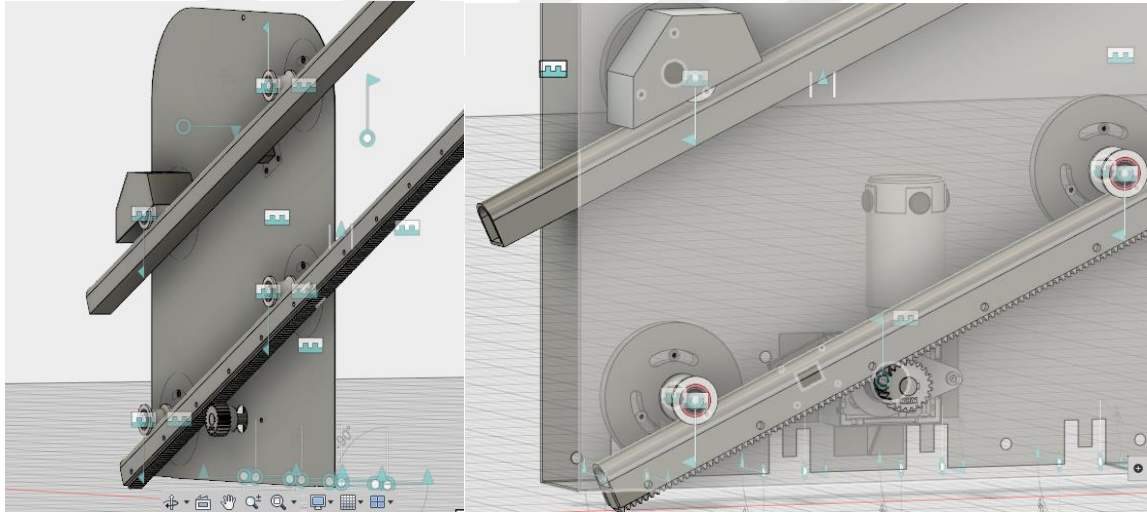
Kremayer ve pinyon dişli CAD çizimi
